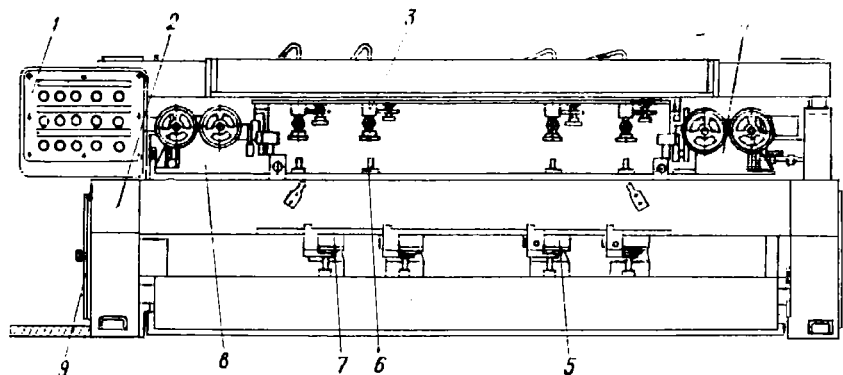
Схема сверлильно-пазовального горизонтально-вертикального станка СГВП-1А:
